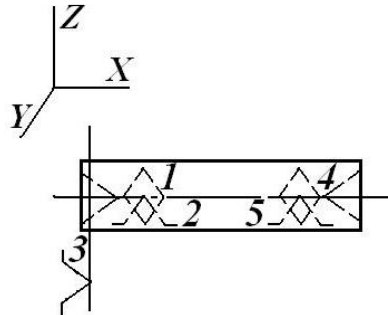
Базування деталі по короткій конічній поверхні (в центрах)
